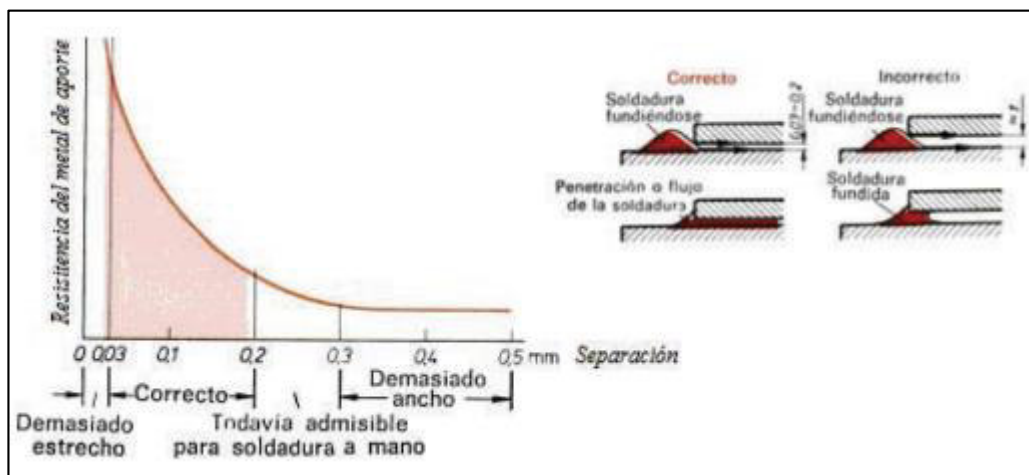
Influencia de la holgura de la junta soldada sobre la resistencia mecánica. (Fuente: [17])
